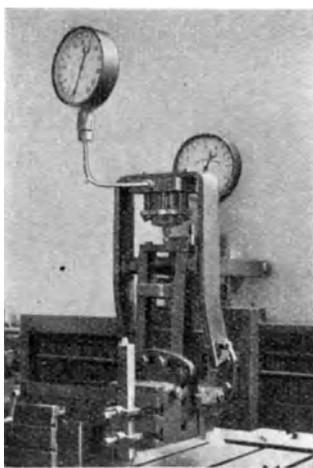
Zwei-Komponenten-Meß-Support für die Tischhobelmaschine.
